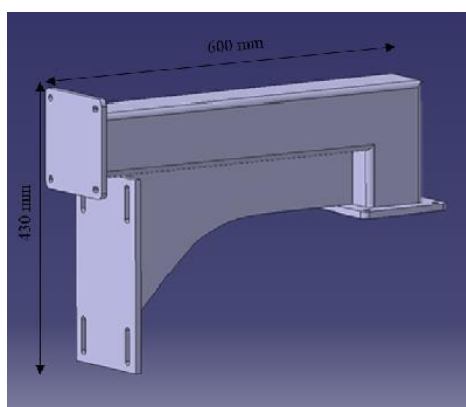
Estrutura de fixação do Conjunto Rampa-Motor
